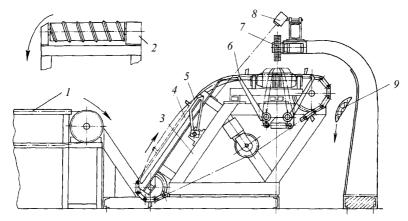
Устройство для поштучной выдачи досок на обрезной станок: I – поперечный конвейер; 2 – роликовый конвейер; 3 – рама; 4 – цепной конвейер; 5 – сбрасыватель досок (горбылей); 6 – центрирующее устройство; 7 – прижим; 8 – датчик наличия сортимента; 9 – сброшенный горбыль
